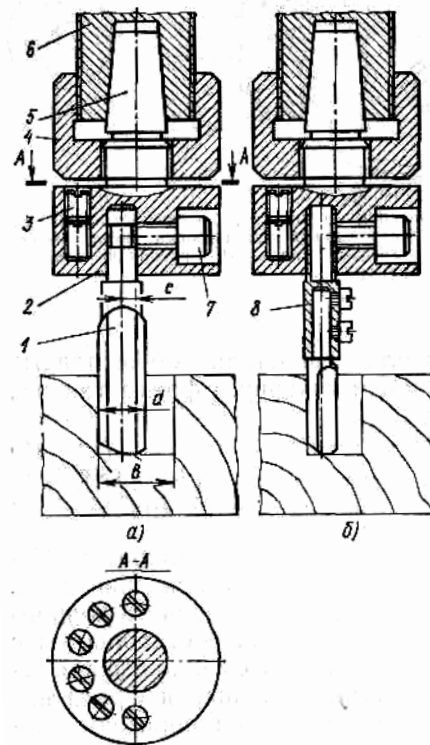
Крепление в патроне концевой фрезы диаметром: *а* — более 7 мм, *б* — менее 7 мм; 1 — фреза, 2 — корпус патрона, 3 — балансировочный винт, 4 — гайка, 5 — хвостовик, 6 — шпиндель, 7 — винт крепления фрезы, 8 — переходная втулка
